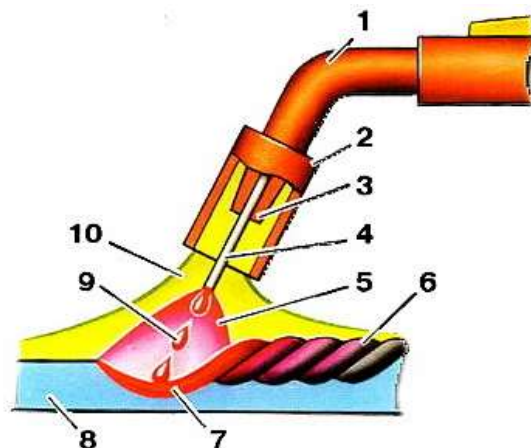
Схема процесу напівавтоматичного зварювання
